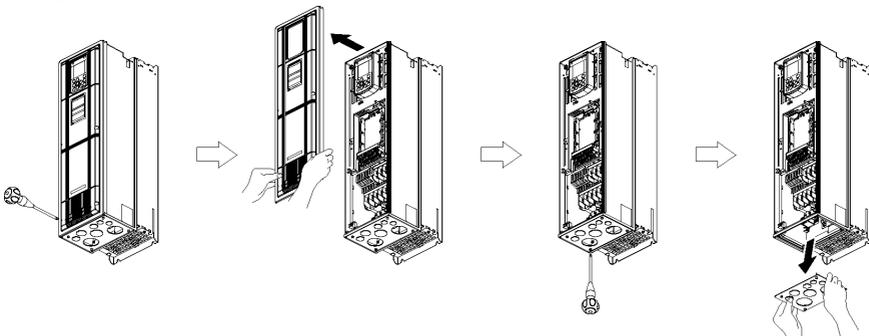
Extracción de la placa frontal y de la placa del cableado (FRN37AQ1M-4□)
